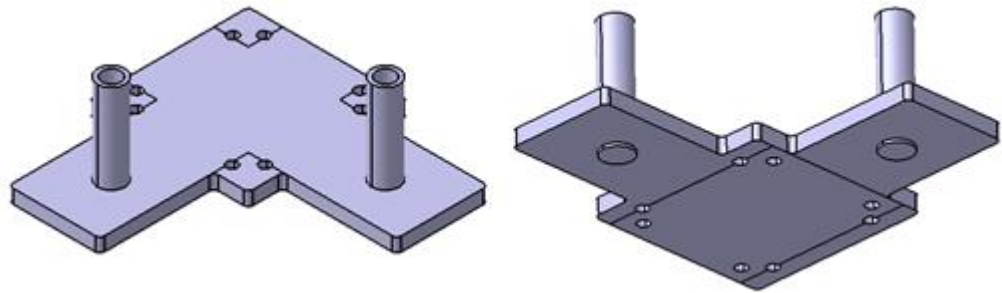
Adaptación de la geometría a las C.C.; se añaden rebajes de 0,01mm en caras de fijación.
